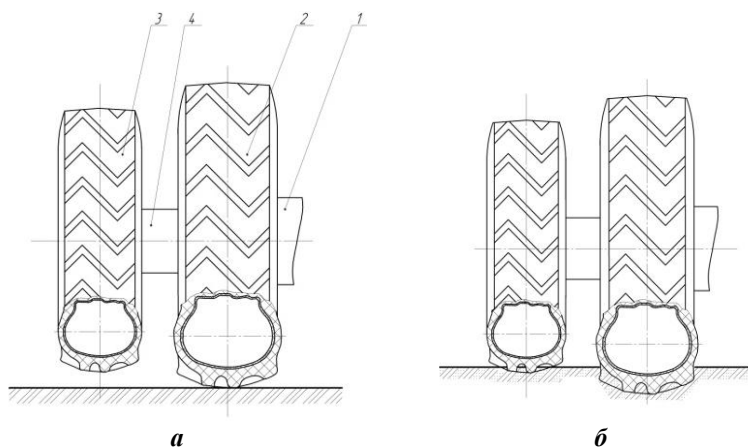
Колёсный движитель с колёсами разного диаметра при движении по твёрдой (а) и деформирующейся опорной поверхности (б):
